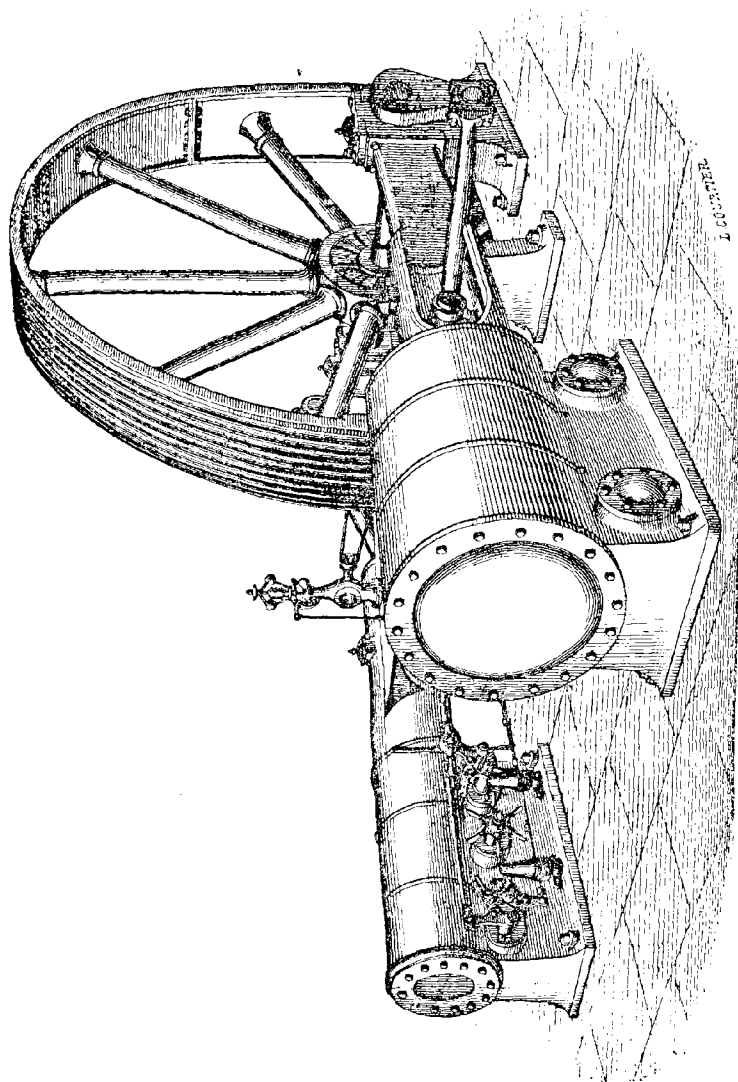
Machine de Quillacq (type Wheelock) (vue perspective).
